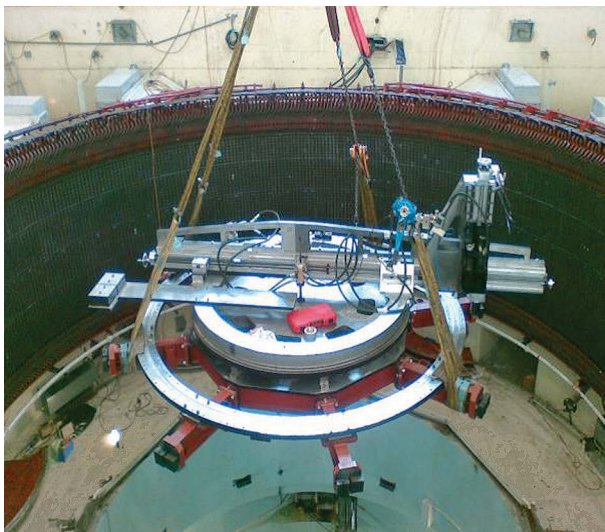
Установка мобильного станка для ремонта блока гидростанции
